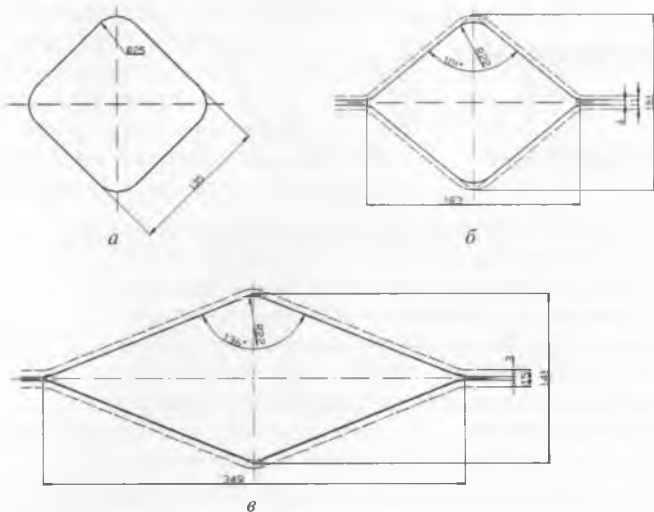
Вид заготовки (а) и инструмента (б, в) для моделирования прокатки квадратной заготовки в ромбическом калибре
